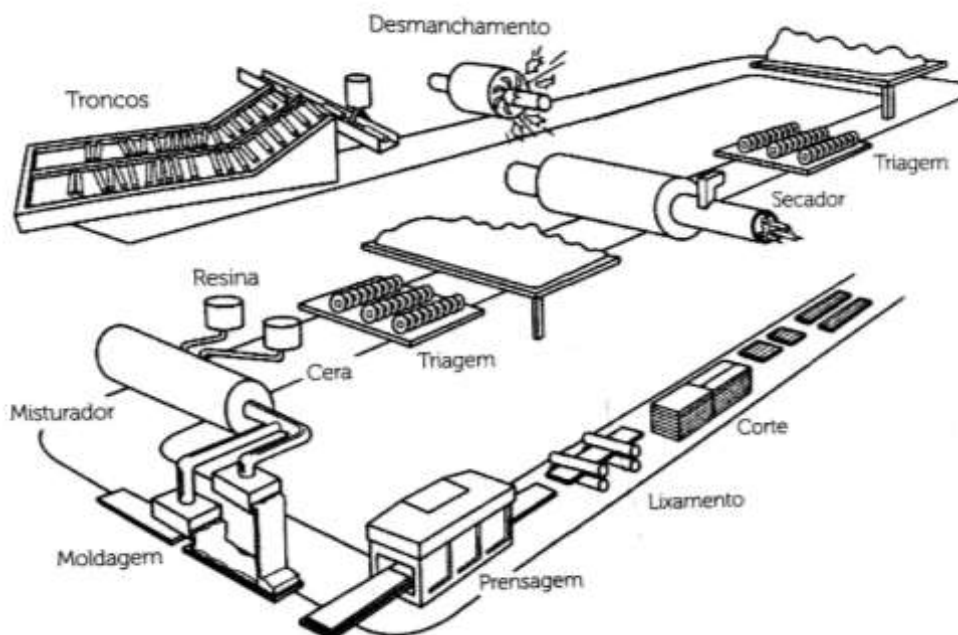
Produção de LSL. Autor: Paulo Barreto Cachim
